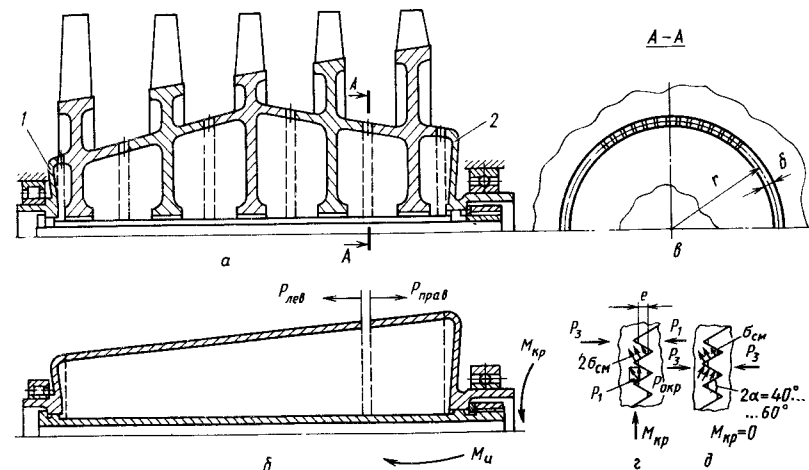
Схема ротора барабанно-дискового типа, секции которого соединяются с помощью торцевых шлиц:
